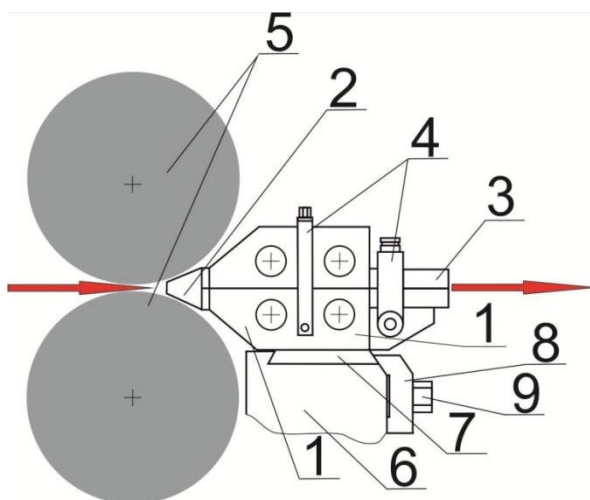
Схема установки НДУ в линии стана (1 - делительное устройство; 2 - вводной пропуск; 3 - выводная шестиручьева проводка; 4 - крепежная скоба с болтом и контргайкой; 5 - прокатные валки; 6 - брус прокатной клетки; 7 - основание; 8, 9 - скоба и болтовое соединение узла крепления делительного устройства на брус; 10 – корпус)
